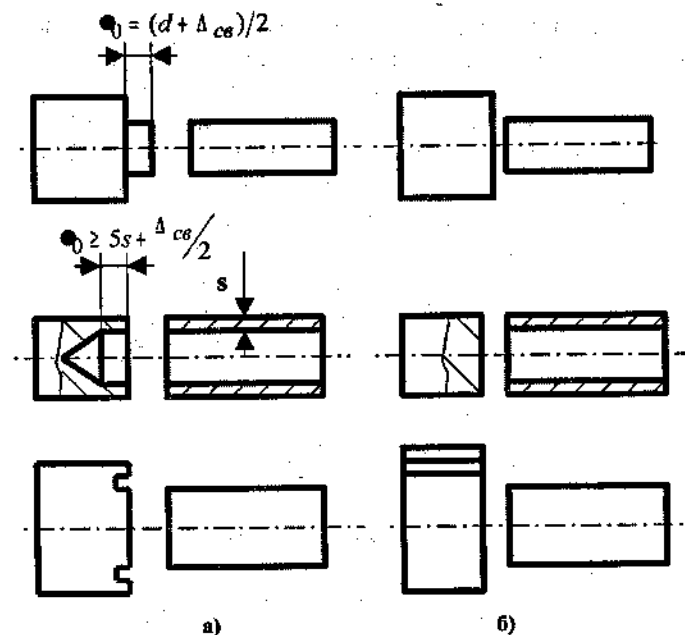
Форма торцов деталей для сварки оплавлением: а) рациональная, б) нерациональная ($\Delta_{\text{св}}$ – суммарное укорочение деталей при сварке)
